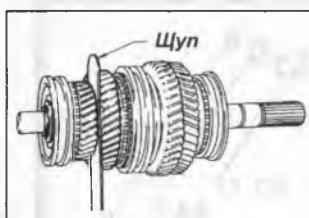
Шестерни 1-ой, 2-ой передач и заднего хода.
